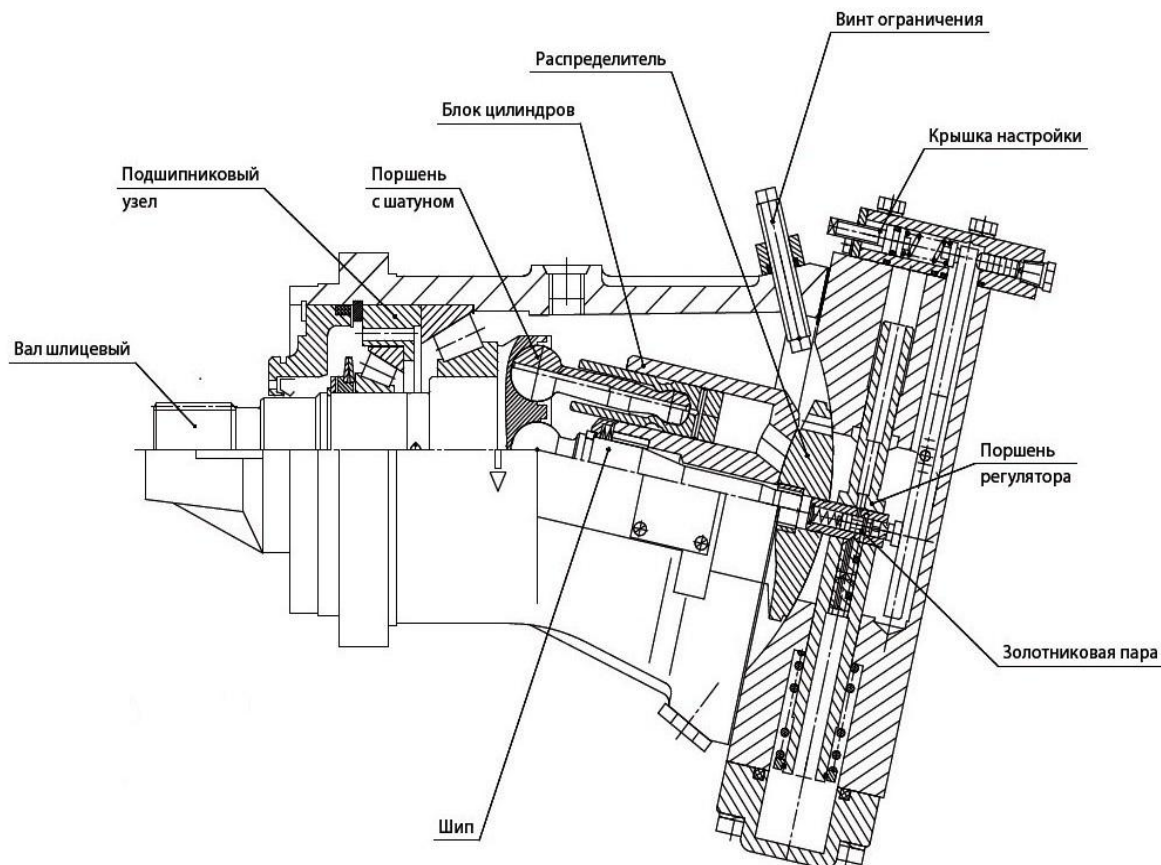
Регулируемый аксиально-поршневой гидромотор типа 313.56
